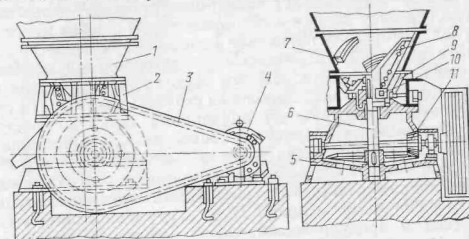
Фрезерная стружкодробилка СК-2М
